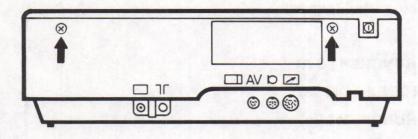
Befestigungsschrauben für Gehäuseoberteil
